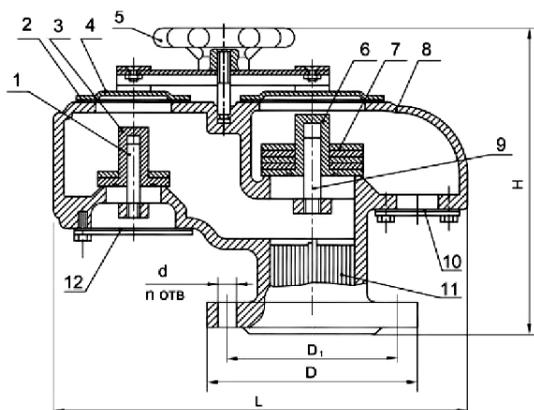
Клапан тип СМДК: 1 – направляющий стержень; 2 – прокладка; 3 – тарелка; 4 – крышка; 5 – специальное устройство; 6 – тарелка; 7 – груз; 8 – корпус; 9 – направляющий стержень; 10, 12 – сетка; 11 – кассета
